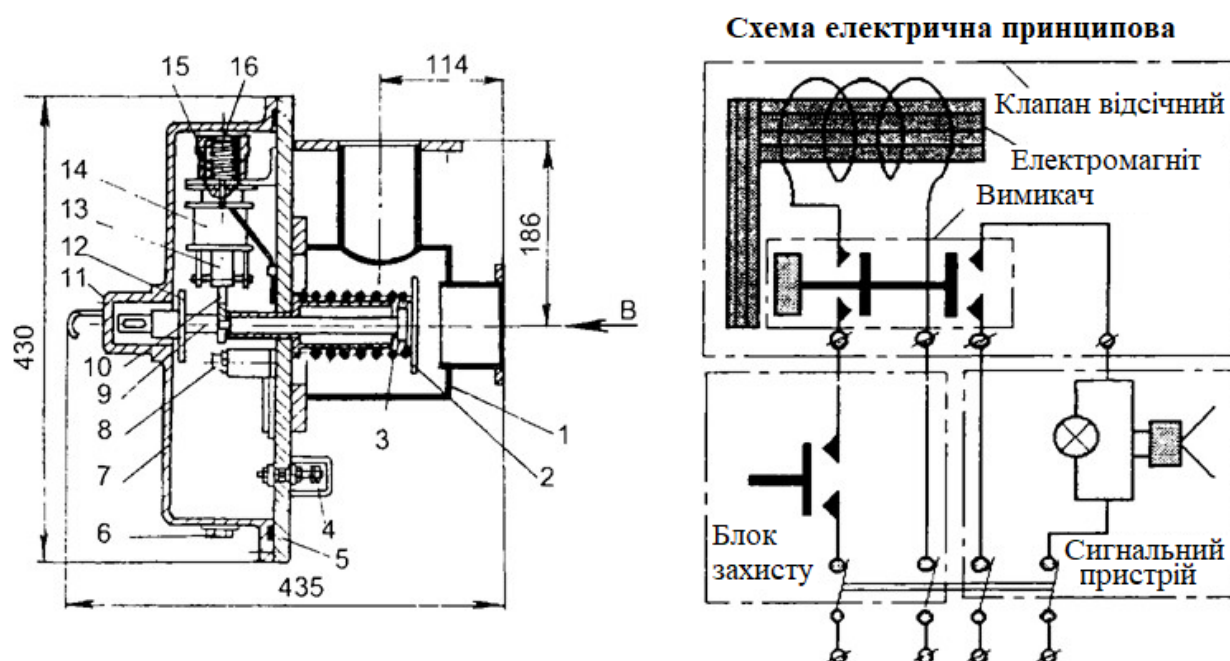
Відсічний клапан: 1- корпус; 2- клапан; 3- пружина; 4- контакти; 5- плита; 6- пробка; 7- кожух; 8- кнопка; 9- тяга; 10- виделка; 11- склянка; 12- диск; 13- якір; 14- електромагніт; 15 - гайка; 16- пружина
